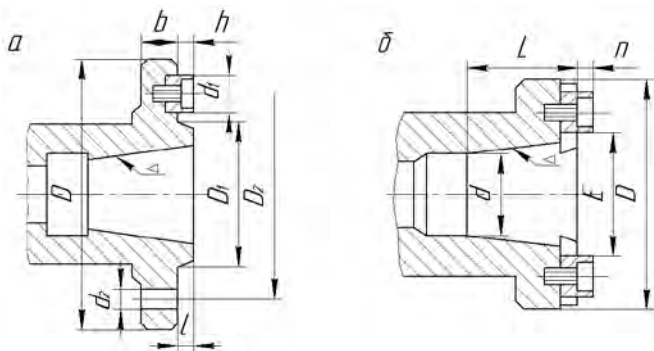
Форма передних концов шпинделей под поворотную шайбу с цилиндрической шпонкой для токарных (а) и с двумя призматическими шпонками для фрезерных и многооперационных сверлильно-фрезерно-расточных станков (б)
